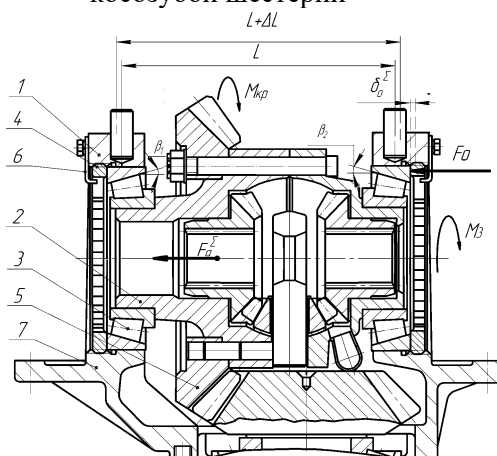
Конструктивная схема дифференциала редуктора в сборе с ведомой шестерней и подшипниками: 1 – крышка, 2 – чашка дифференциала, 3 – конический подшипник, 4 – резьбовое корончатое регулировочное кольцо, 5 – ведомая шестерня, 6 – стопорный элемент регулировочного кольца, 7 – картер редуктора.
